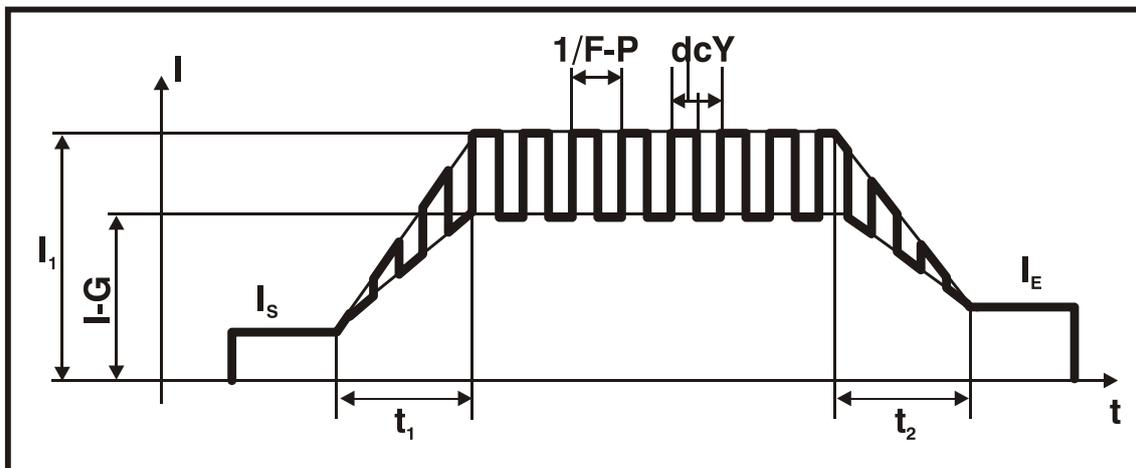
Modo pulsante TIG - curva da corrente de soldagem
